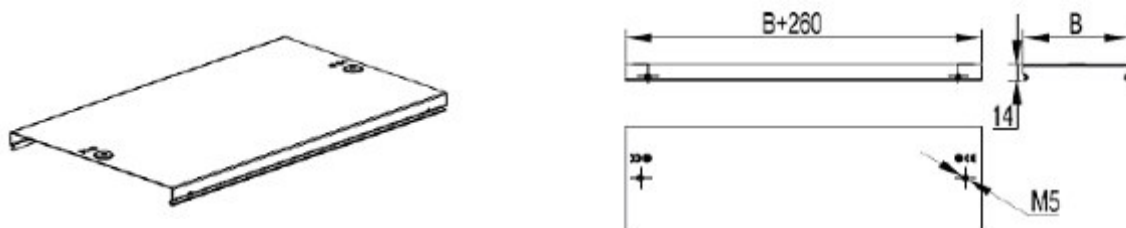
Крышка TD/TDS га ответвитель T-образный вертикальный
